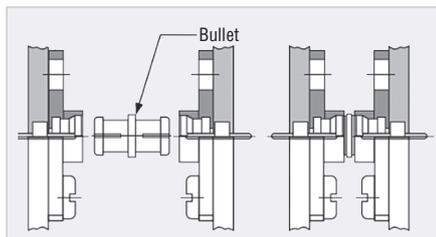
Соединение печатных плат с помощью адаптера «bullet» и двух соединителей SMPM вилка
